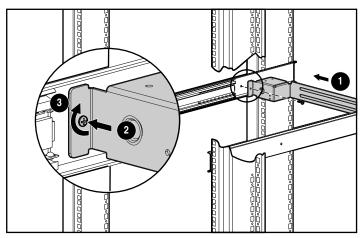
fissaggio del supporto alla staffa di montaggio
